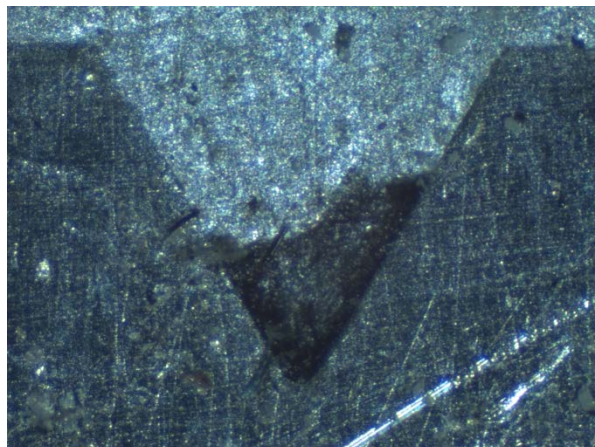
Резьба образованная самозакручивающейся шпилькой
